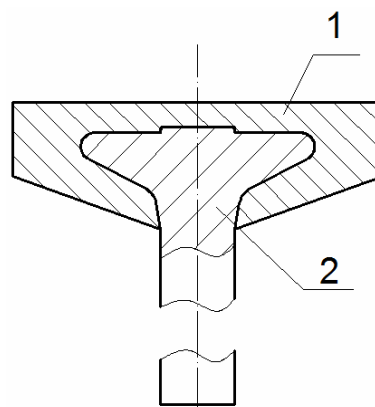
Составная поковка клапана: 1 и 2 – элементы тарелки клапана, полученные соответственно из головной (1) и стержневой (2) заготовок (см. рисунок 1)
